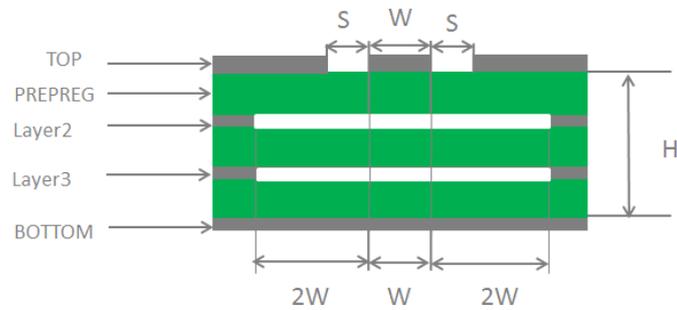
四层 PCB 板共面波导结构 (参考地为第四层)
